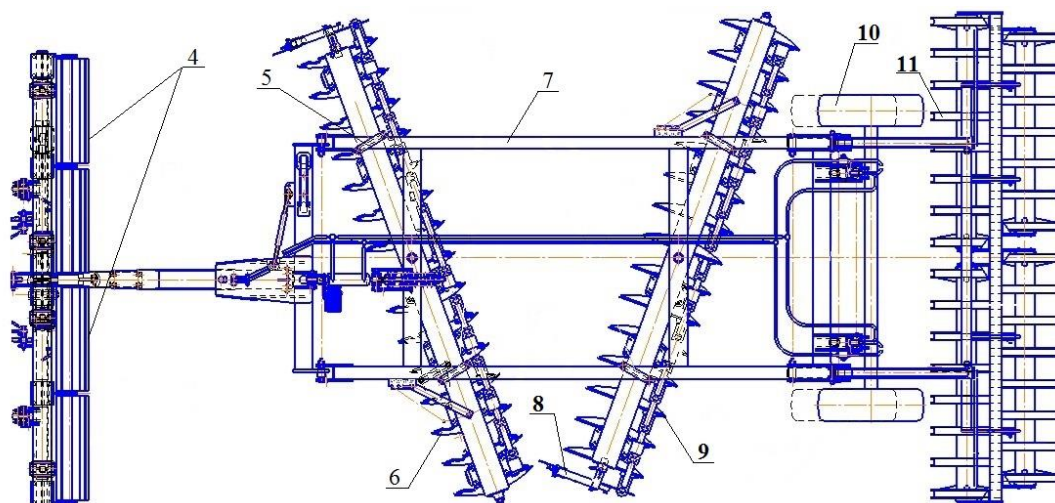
Загальний вигляд (вигляд зверху) дискової борони з катком-подрібнювачем для додаткового подрібнення рослинних решток:
